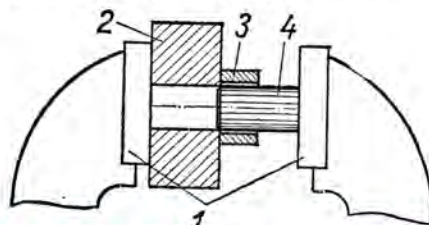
Запрессовка деталей с технологической трубкой: 1 — губки тисков; 2 — основная деталь; 3 — технологическая трубка; 4 — запрессовываемая деталь.
